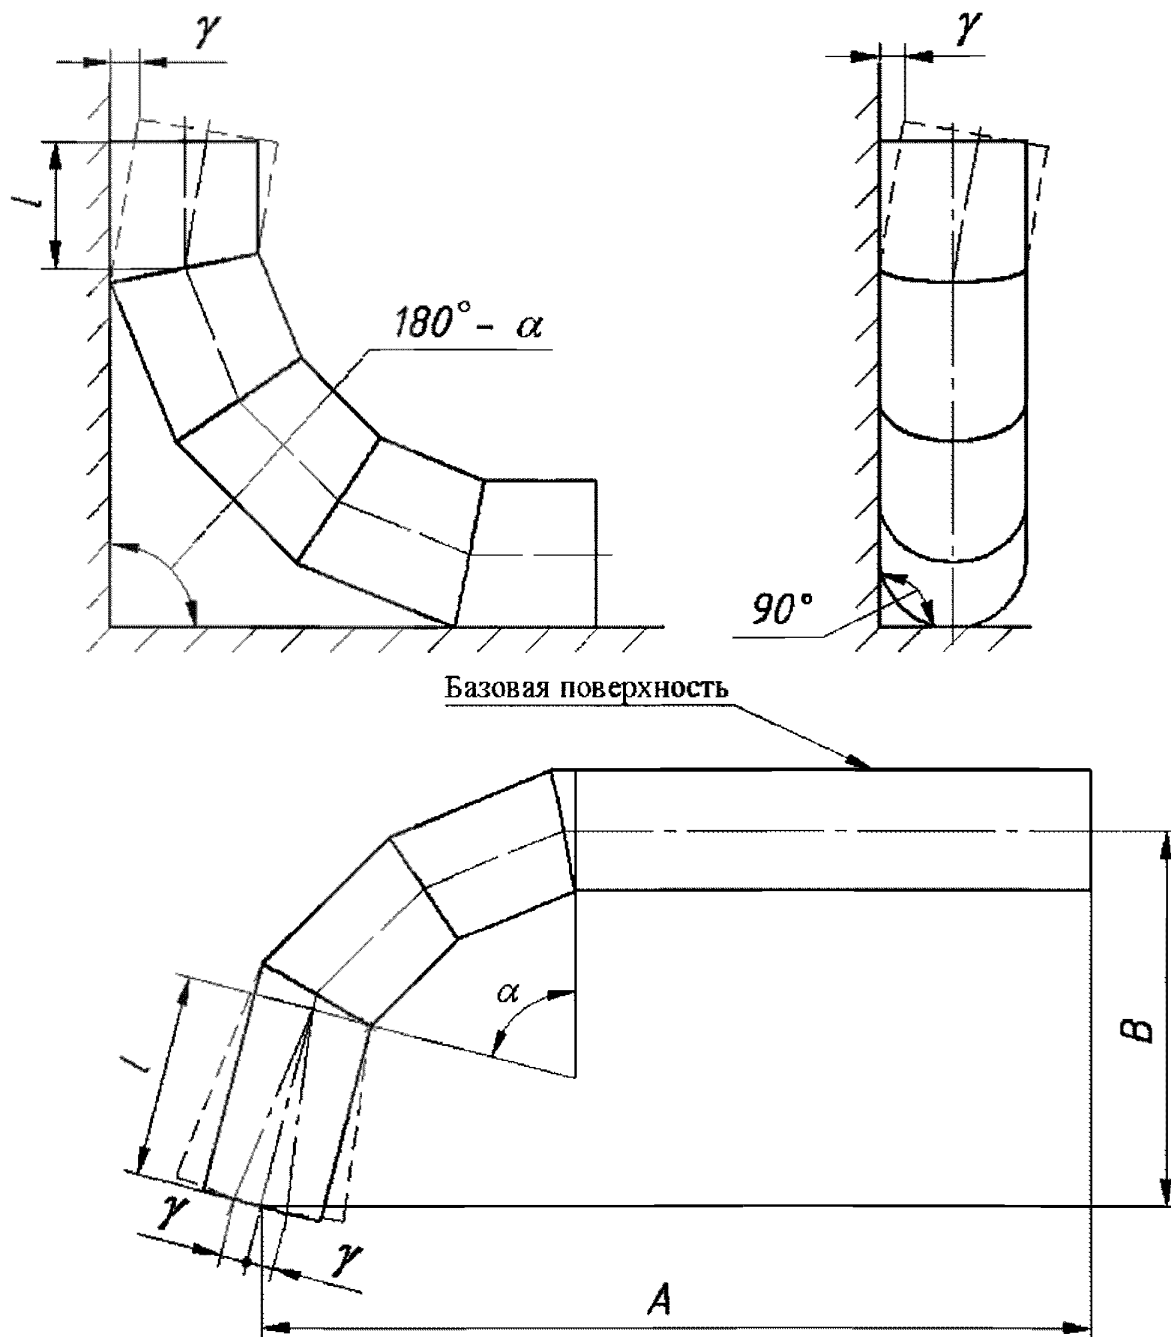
Отклонение от номинального положения оси сварного колена
